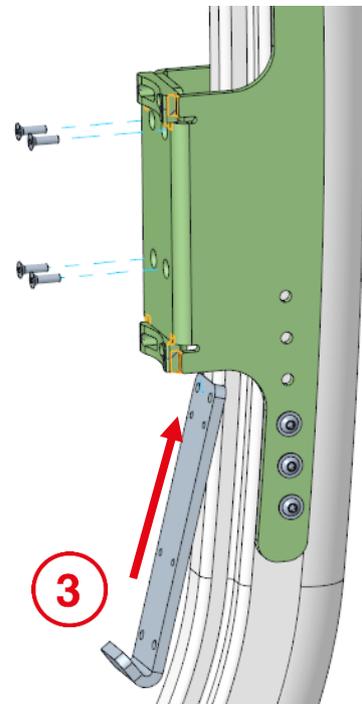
Montage Gewindeplatte; Außenansicht;
